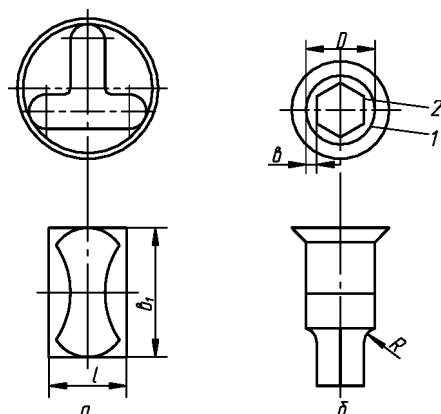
Конструкции пуансонов сложной формы: 1 — контур посадочной поверхности, 2 — контур рабочей поверхности
